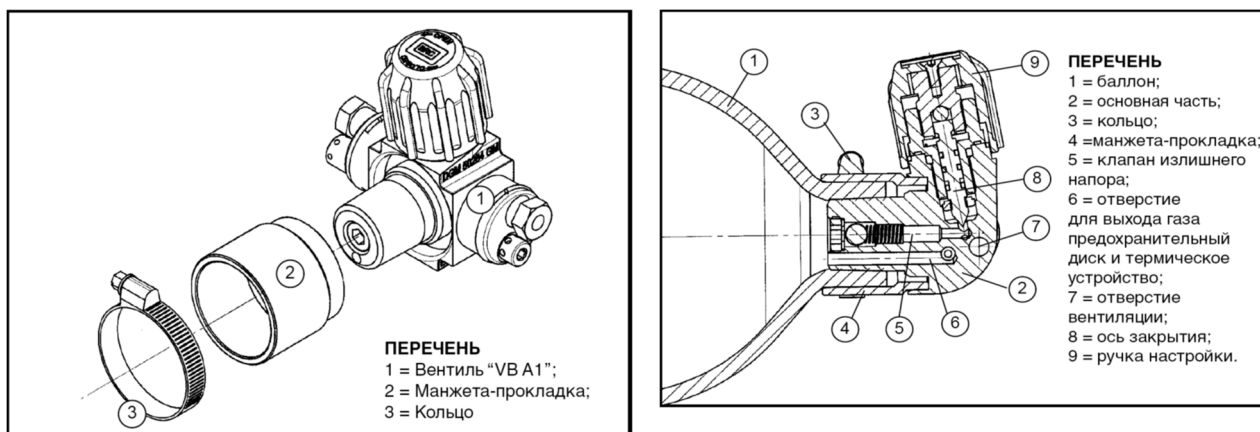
Вентиль «VB A1» общий вид и установка на баллон в разрезе
